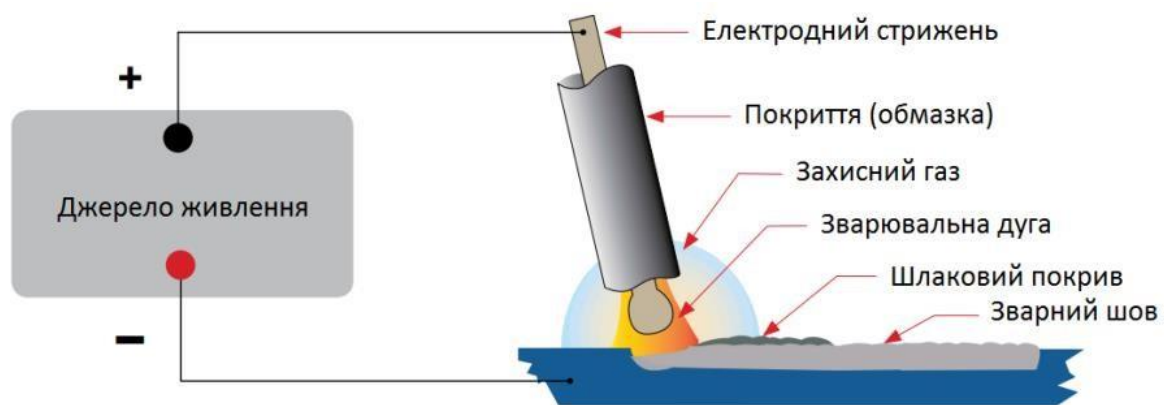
Схема процесу ручного дугового зварювання.
